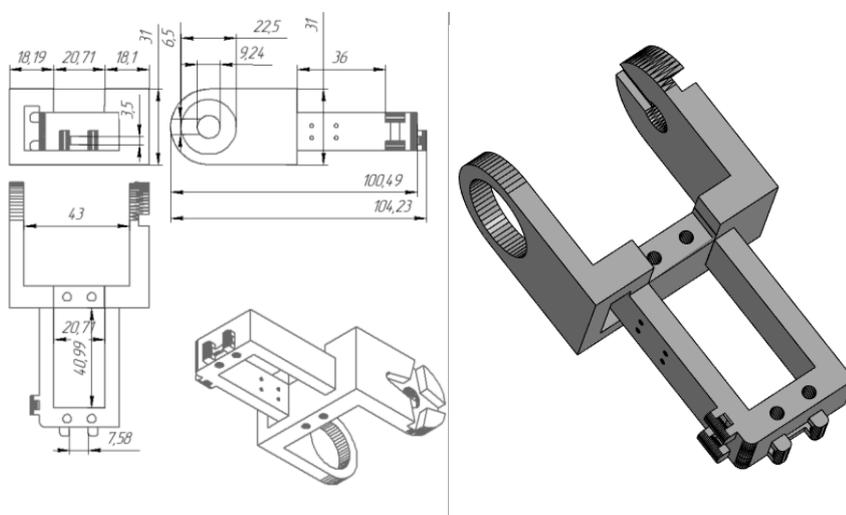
Модель и чертеж модуля конструкции корпуса для улучшенной версии
